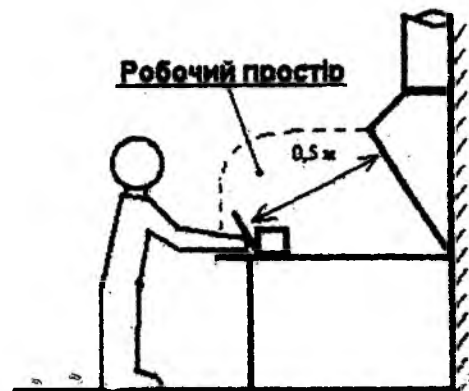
Витяжна вентиляція (зонти) на робочому місці зварювальника
